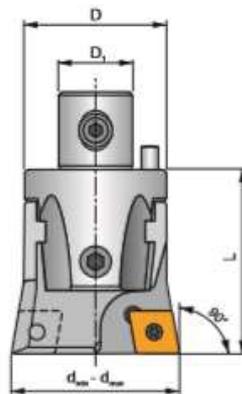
Расточная головка для черновой обработки ф. Pramet
